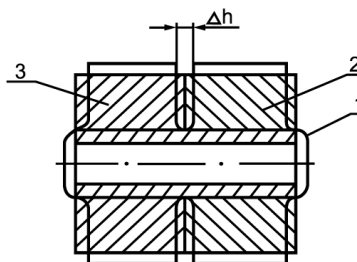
Многоэлементное соединение деталей с натягом и схема деформаций деталей при КТСС: 1 – охватываемая деталь; 2 и 3 – охватывающие детали
